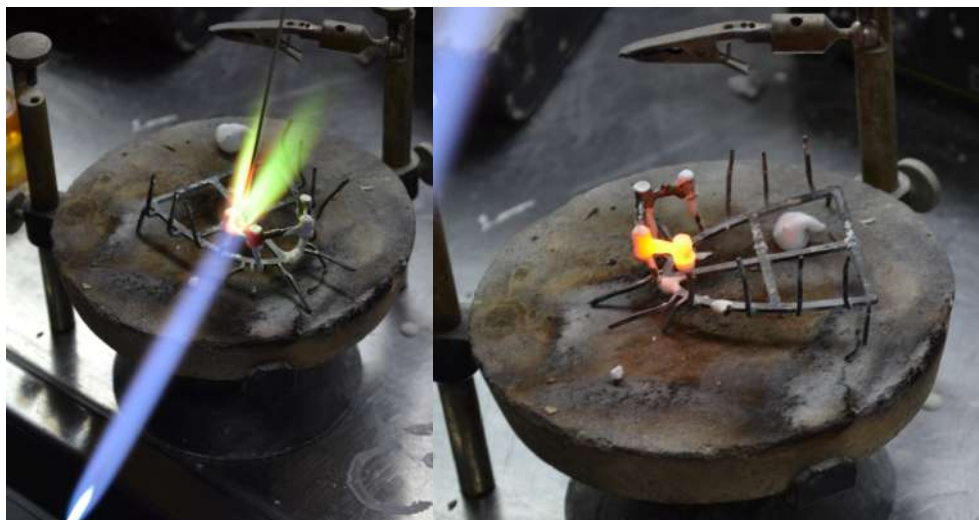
Soldadura de segmentos sobre estructura Clever Spider.
